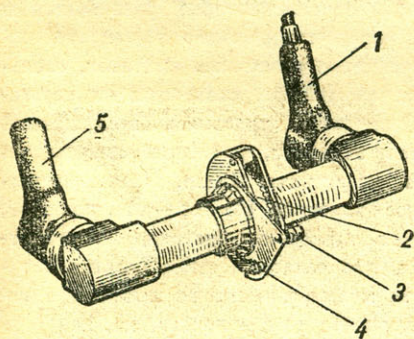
Фреза ремонтника: 1 — рукоять пневмодреши, 2 — фреза, 3 — ролик, 4 — ограничитель, 5 — вспомогательная рукоять.
